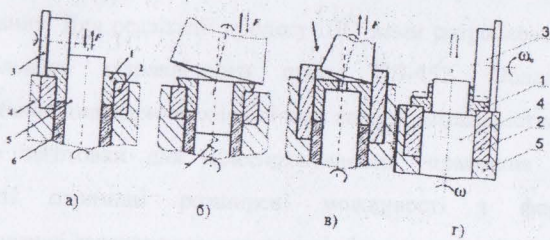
Типові схеми ШО циліндричним і конічним валками: висаджування зовнішнього бурта (а), (б); висаджування внутрішнього бурта (в); висаджування і зворотне витискування елементів заготовки (г)
